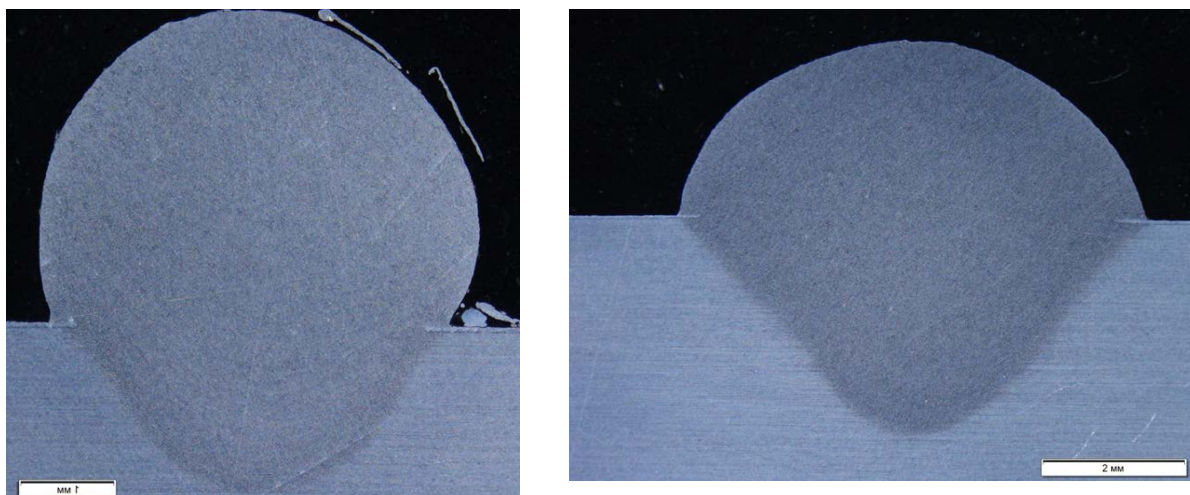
Общий вид образцов: а – СМТ; б – Плазма-МИГ
